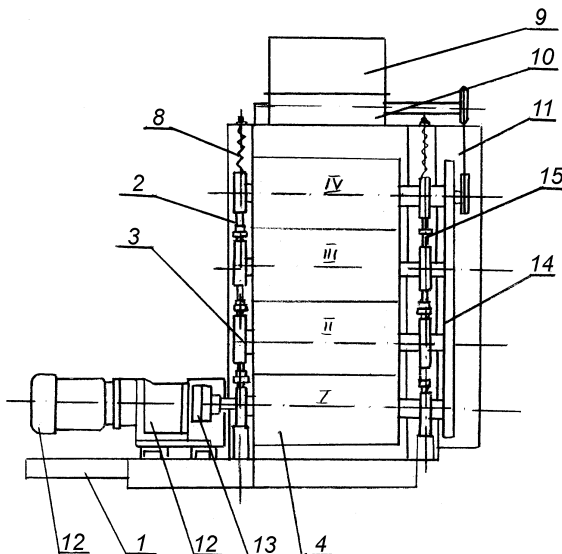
Схеми чотирьох вальцевого станка: 1 – станина; 2 – стійка; 3 – корпус підшипників; 4 – валець; 5 – щитки; 6 – стяжка; 7 – гайка; 8 – підпружинені опори; 9 – бункер; 10 – живильник; 11 – клинопасова передача; 12 – двигун-редуктор; 13 – муфта; 14 – передача циліндрична прямозуба; 15 – домкрати
